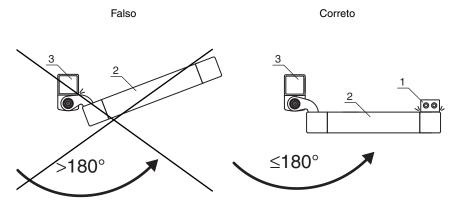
Batente mecânico (1) para a parte móvel do dispositivo de proteção
